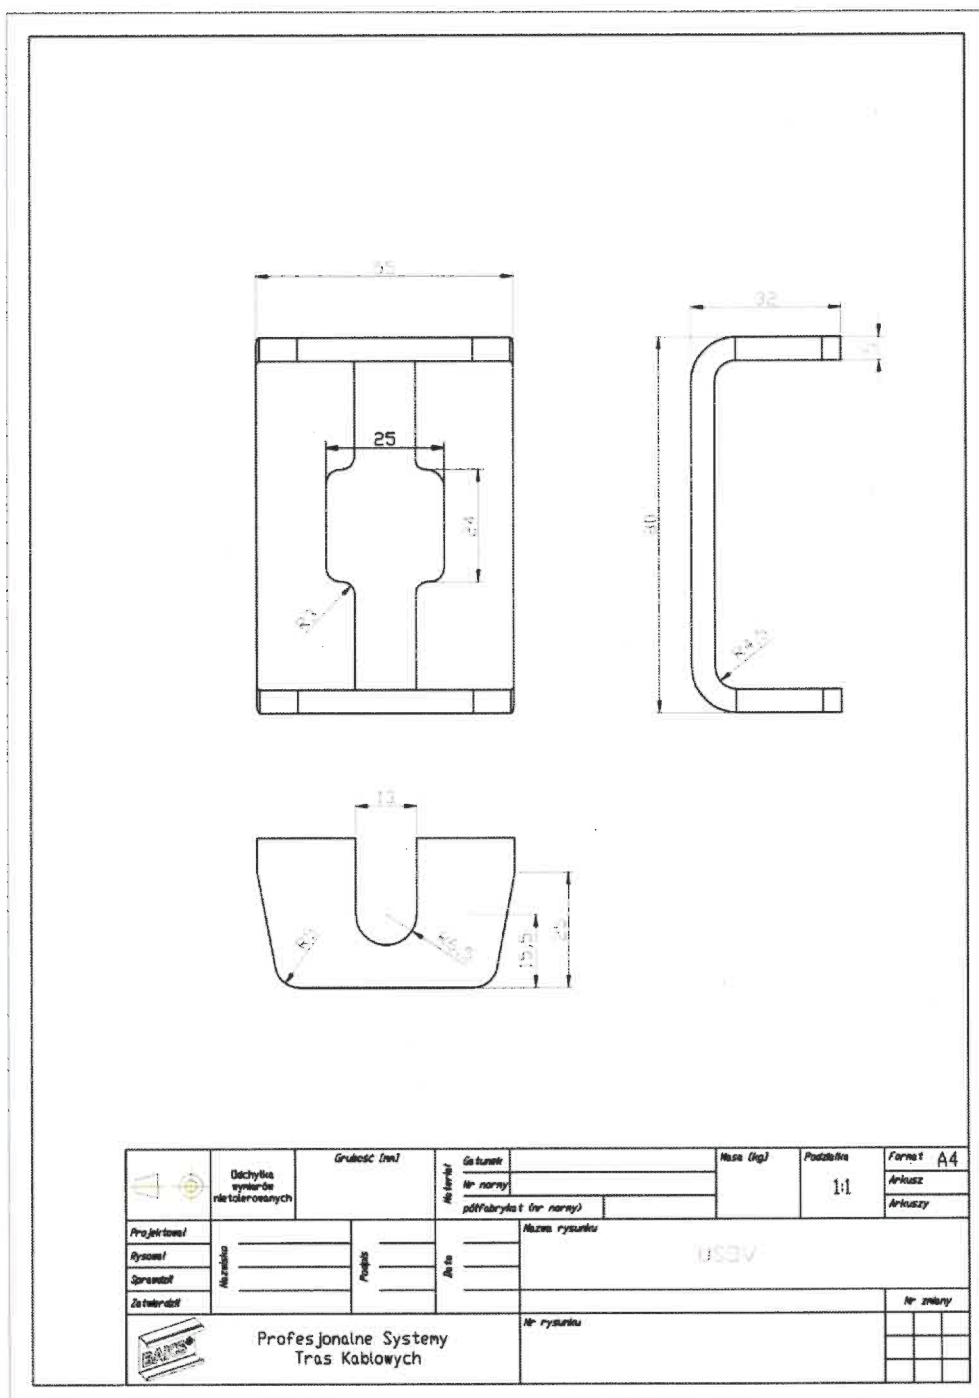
5 Deckenbefestigung der Gewindestange USOV
